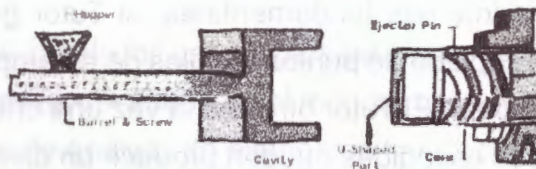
Herramienta del Injection Molding requerida para producir una parte en forma de U
